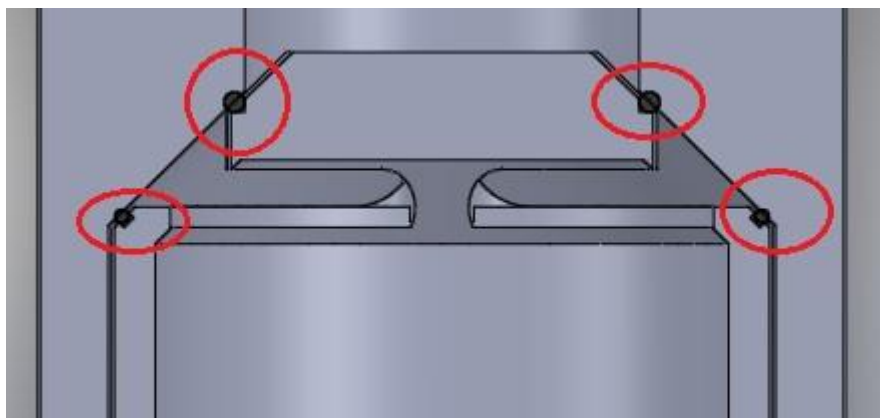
Flange de união entre válvula e tubulação (Fonte: autor).
